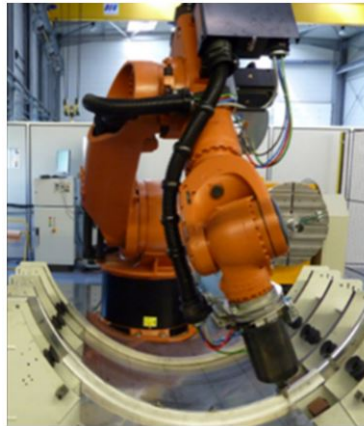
Robot Kuka KR500-2MT de l'Institut de Soudure de Goin
